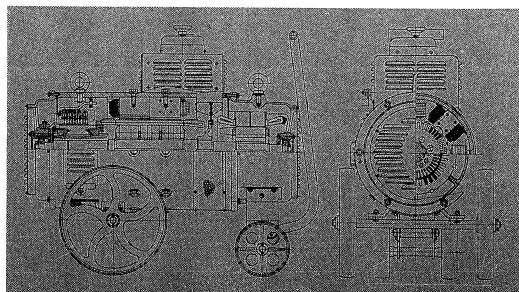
Общий вид (разрез) преобразователя типа ПС-500
